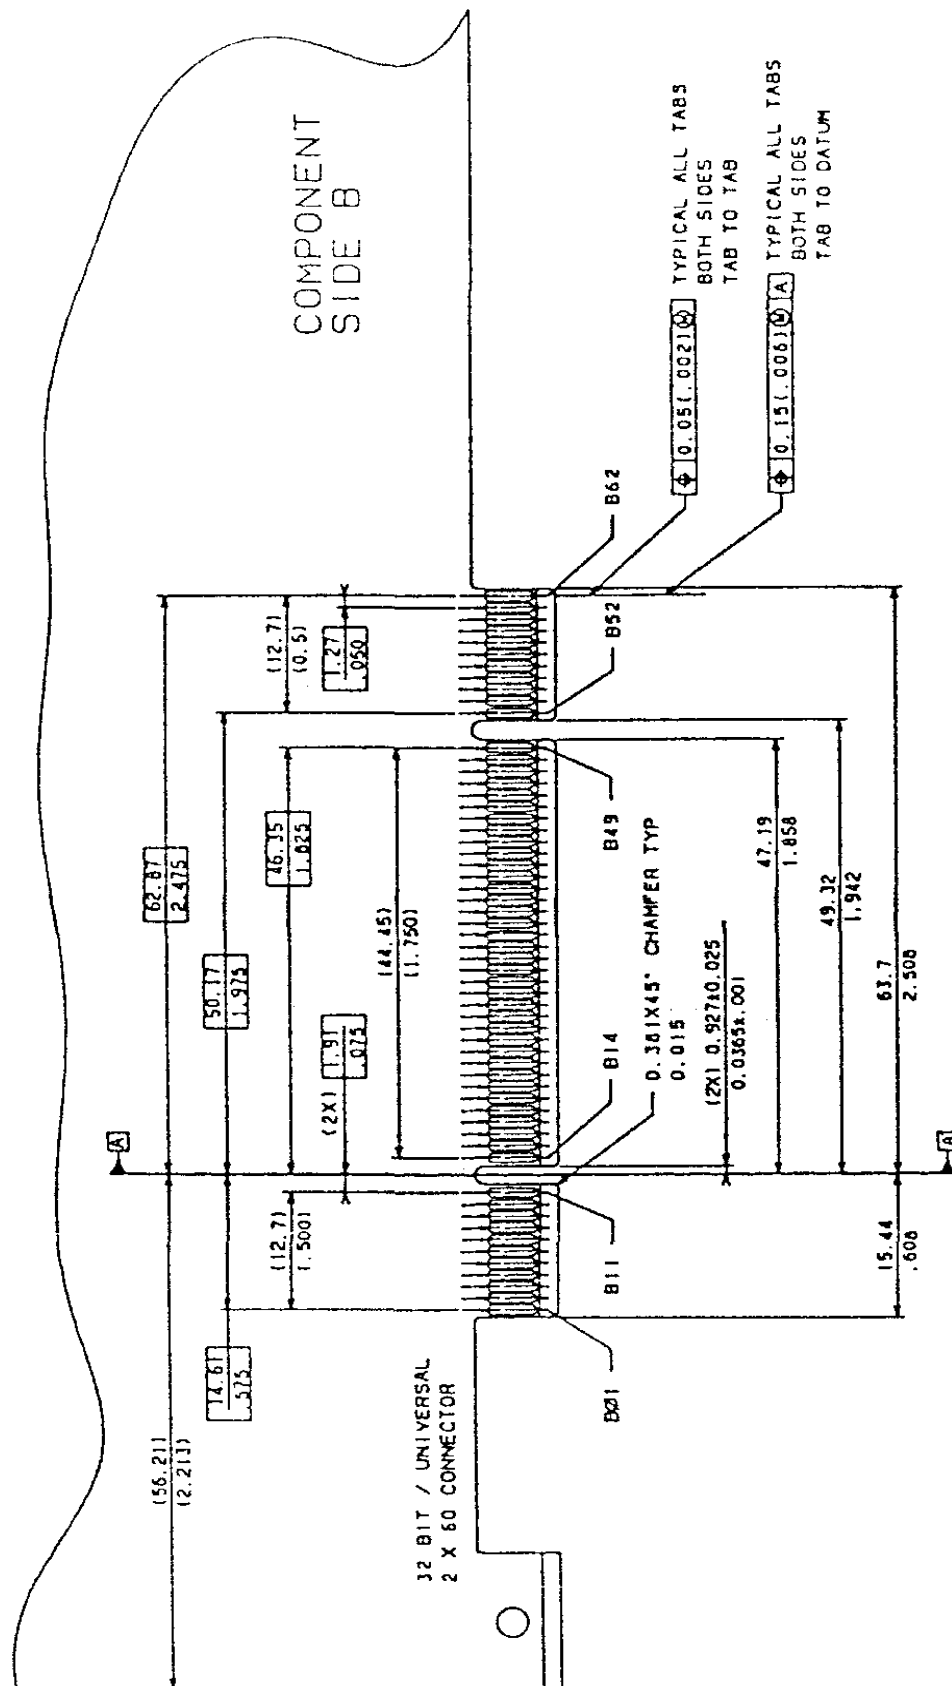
Размеры универсального соединительного устройства для 32-битовых плат и допуски
